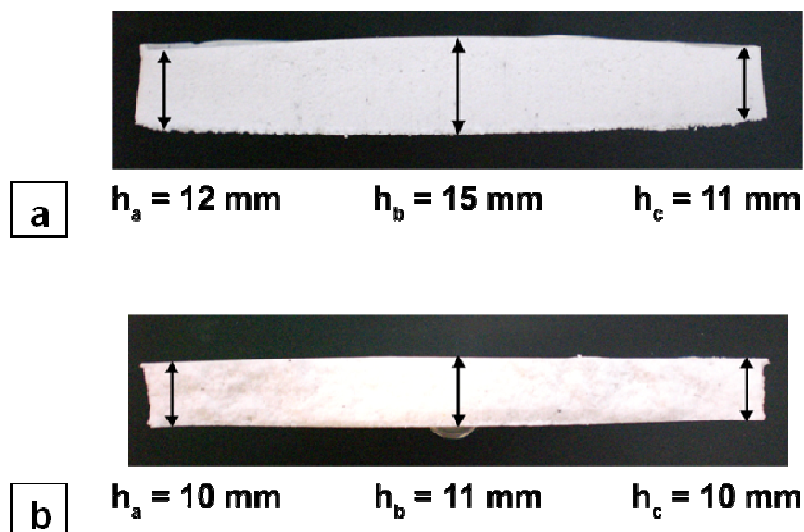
Großvolumiger Formkörper im Querschnitt: a) in einer PTFE-Form und b) in einer makroporösen Aluminiumform aufgeschäumt.
